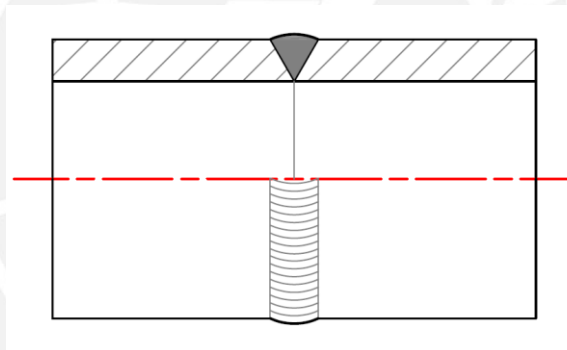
Tubería soldada circunferencialmente.
